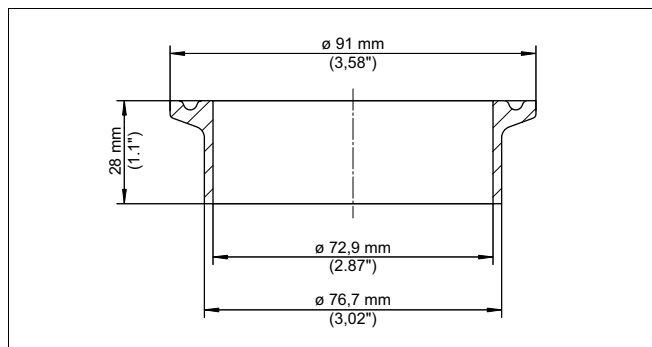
Размеры приварного штуцера - зажим 3" PN16 ($\varnothing 91 \text{ mm}$) DIN 32676, ISO 2852/316L
